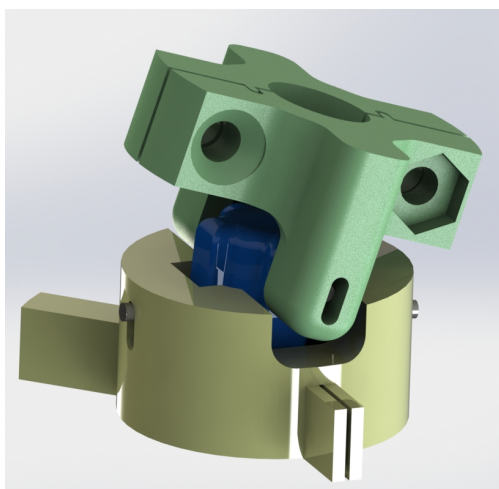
Cardan utilizado para acoplar o motor à válvula
